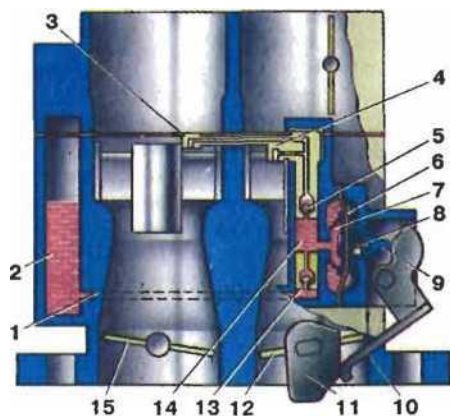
Схема ускорительного насоса карбюратора ДААЗ-2108: 1 - топливный канал; 2 - поплавковая камера; 3,4 - распылители вторичной и первичной камер; 5 - обратный клапан; 6 - диафрагма; 7 - пружина диафрагмы; 8 - демпфирующая пружина; 9 - толкатель; 10 - рычаг привода; 11 - кулачок привода; 12 - дроссельная заслонка первичной камеры; 13 - всасывающий клапан; 14 - нагнетательный канал; 15 - дроссельная заслонка вторичной камеры насосом из поплавковой камеры.
